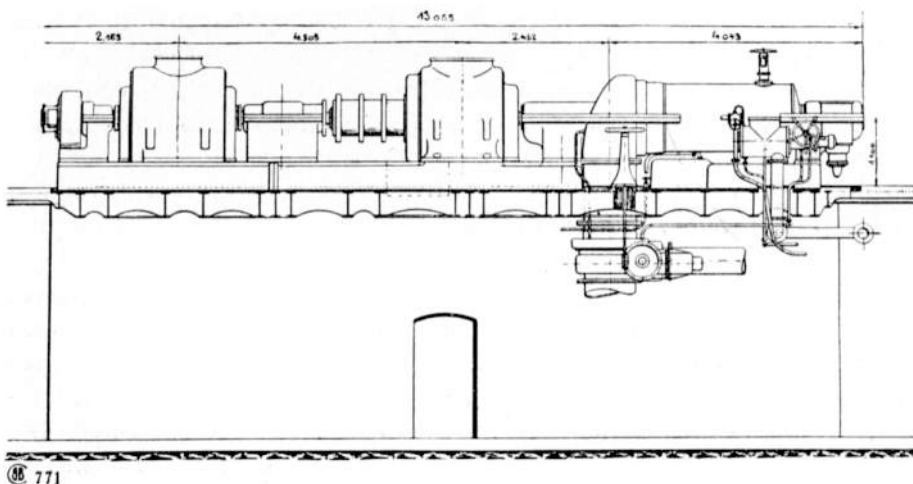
Turbomaschinensatz für die Fördermaschine auf Heinitzgrube.
